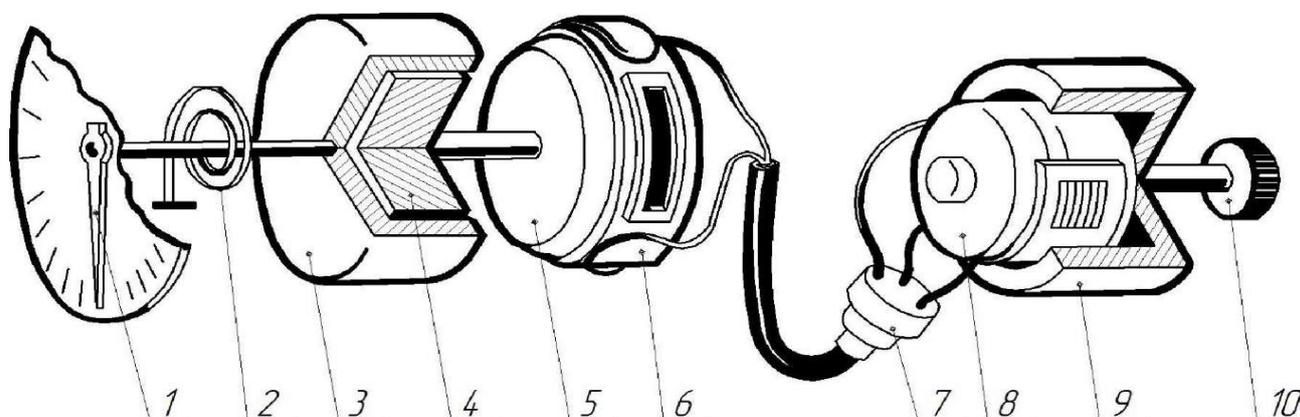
Электрический тахометр 1 - Стрелка; 2 - Спиральная пружина; 3 - Измерительный преобразователь; 4 - Магнитный узел;
